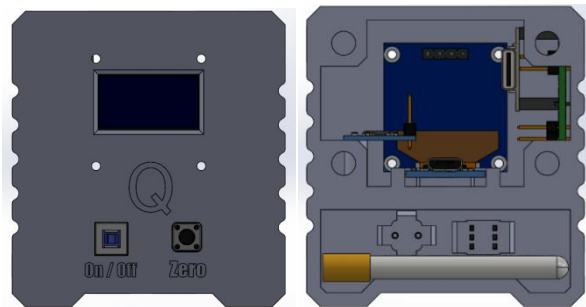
Diseño CAD goniómetro, imagen del autor.
